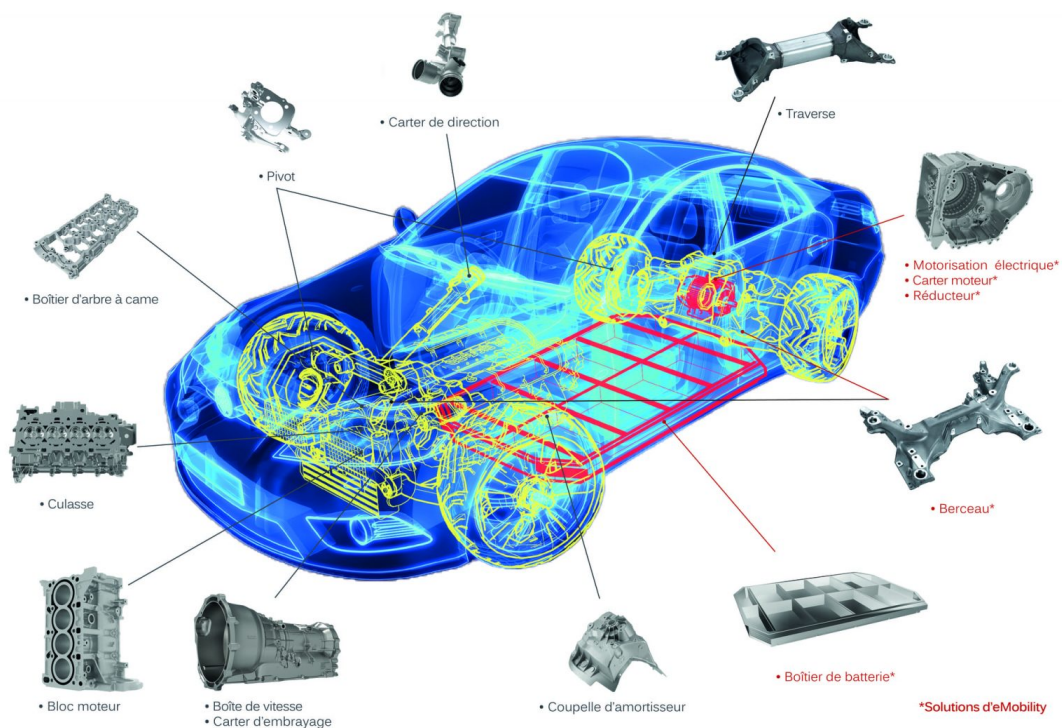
Pièces cibles de PCI MACHINING, source : PCI MACHINING
